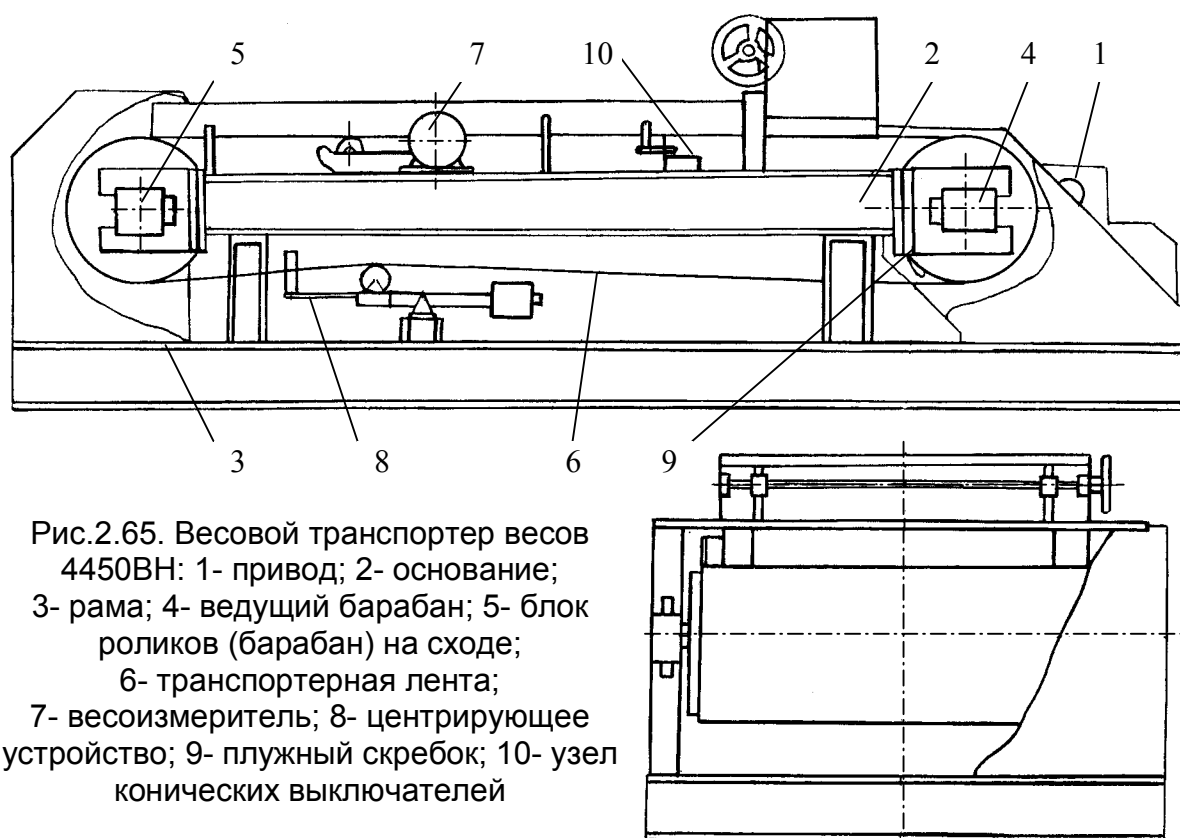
Весовой транспортер весов 4450ВН: 1- привод; 2- основание; 3- рама; 4- ведущий барабан; 5- блок роликов (барабан) на сходе; 6- транспортерная лента; 7- весоизмеритель; 8- центрирующее устройство; 9- плужный скребок; 10- узел конических выключателей
